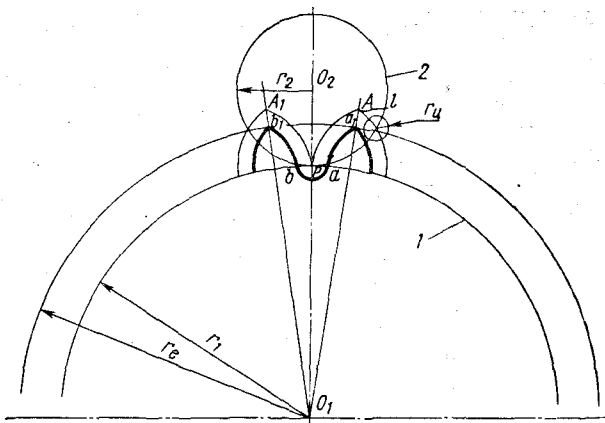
Профиль головки зуба колеса теоретический и действительный (эквидистантный)
